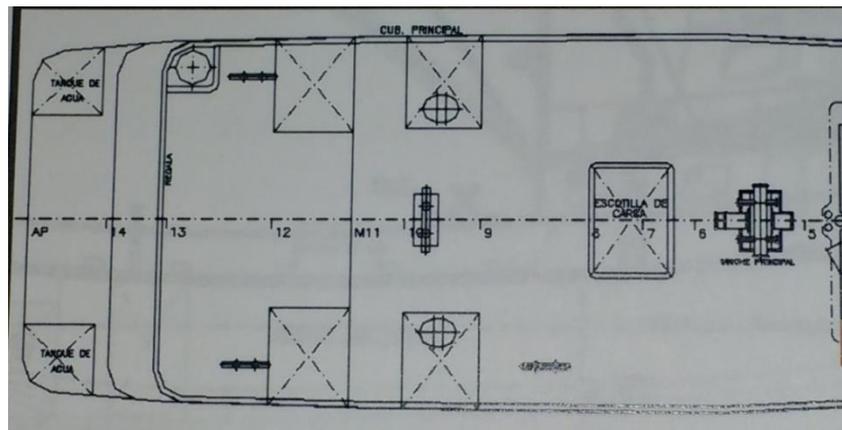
Cubierta de carga sin soportes laterales. Fuente: Copeinca Flota
